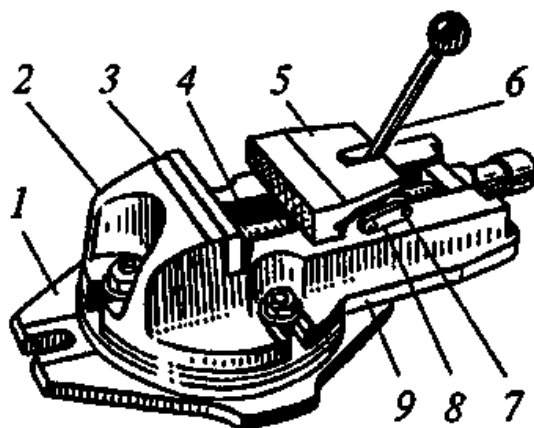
Быстродействующие машинные тиски: 1 – корпус; 2 – поворотная часть; 3 – неподвижная губка; 4 – винт; 5 – губка; 6 – рукоятка; 7 – эксцентриковый вал; 8 – двойной кулачок; 9 – основание
